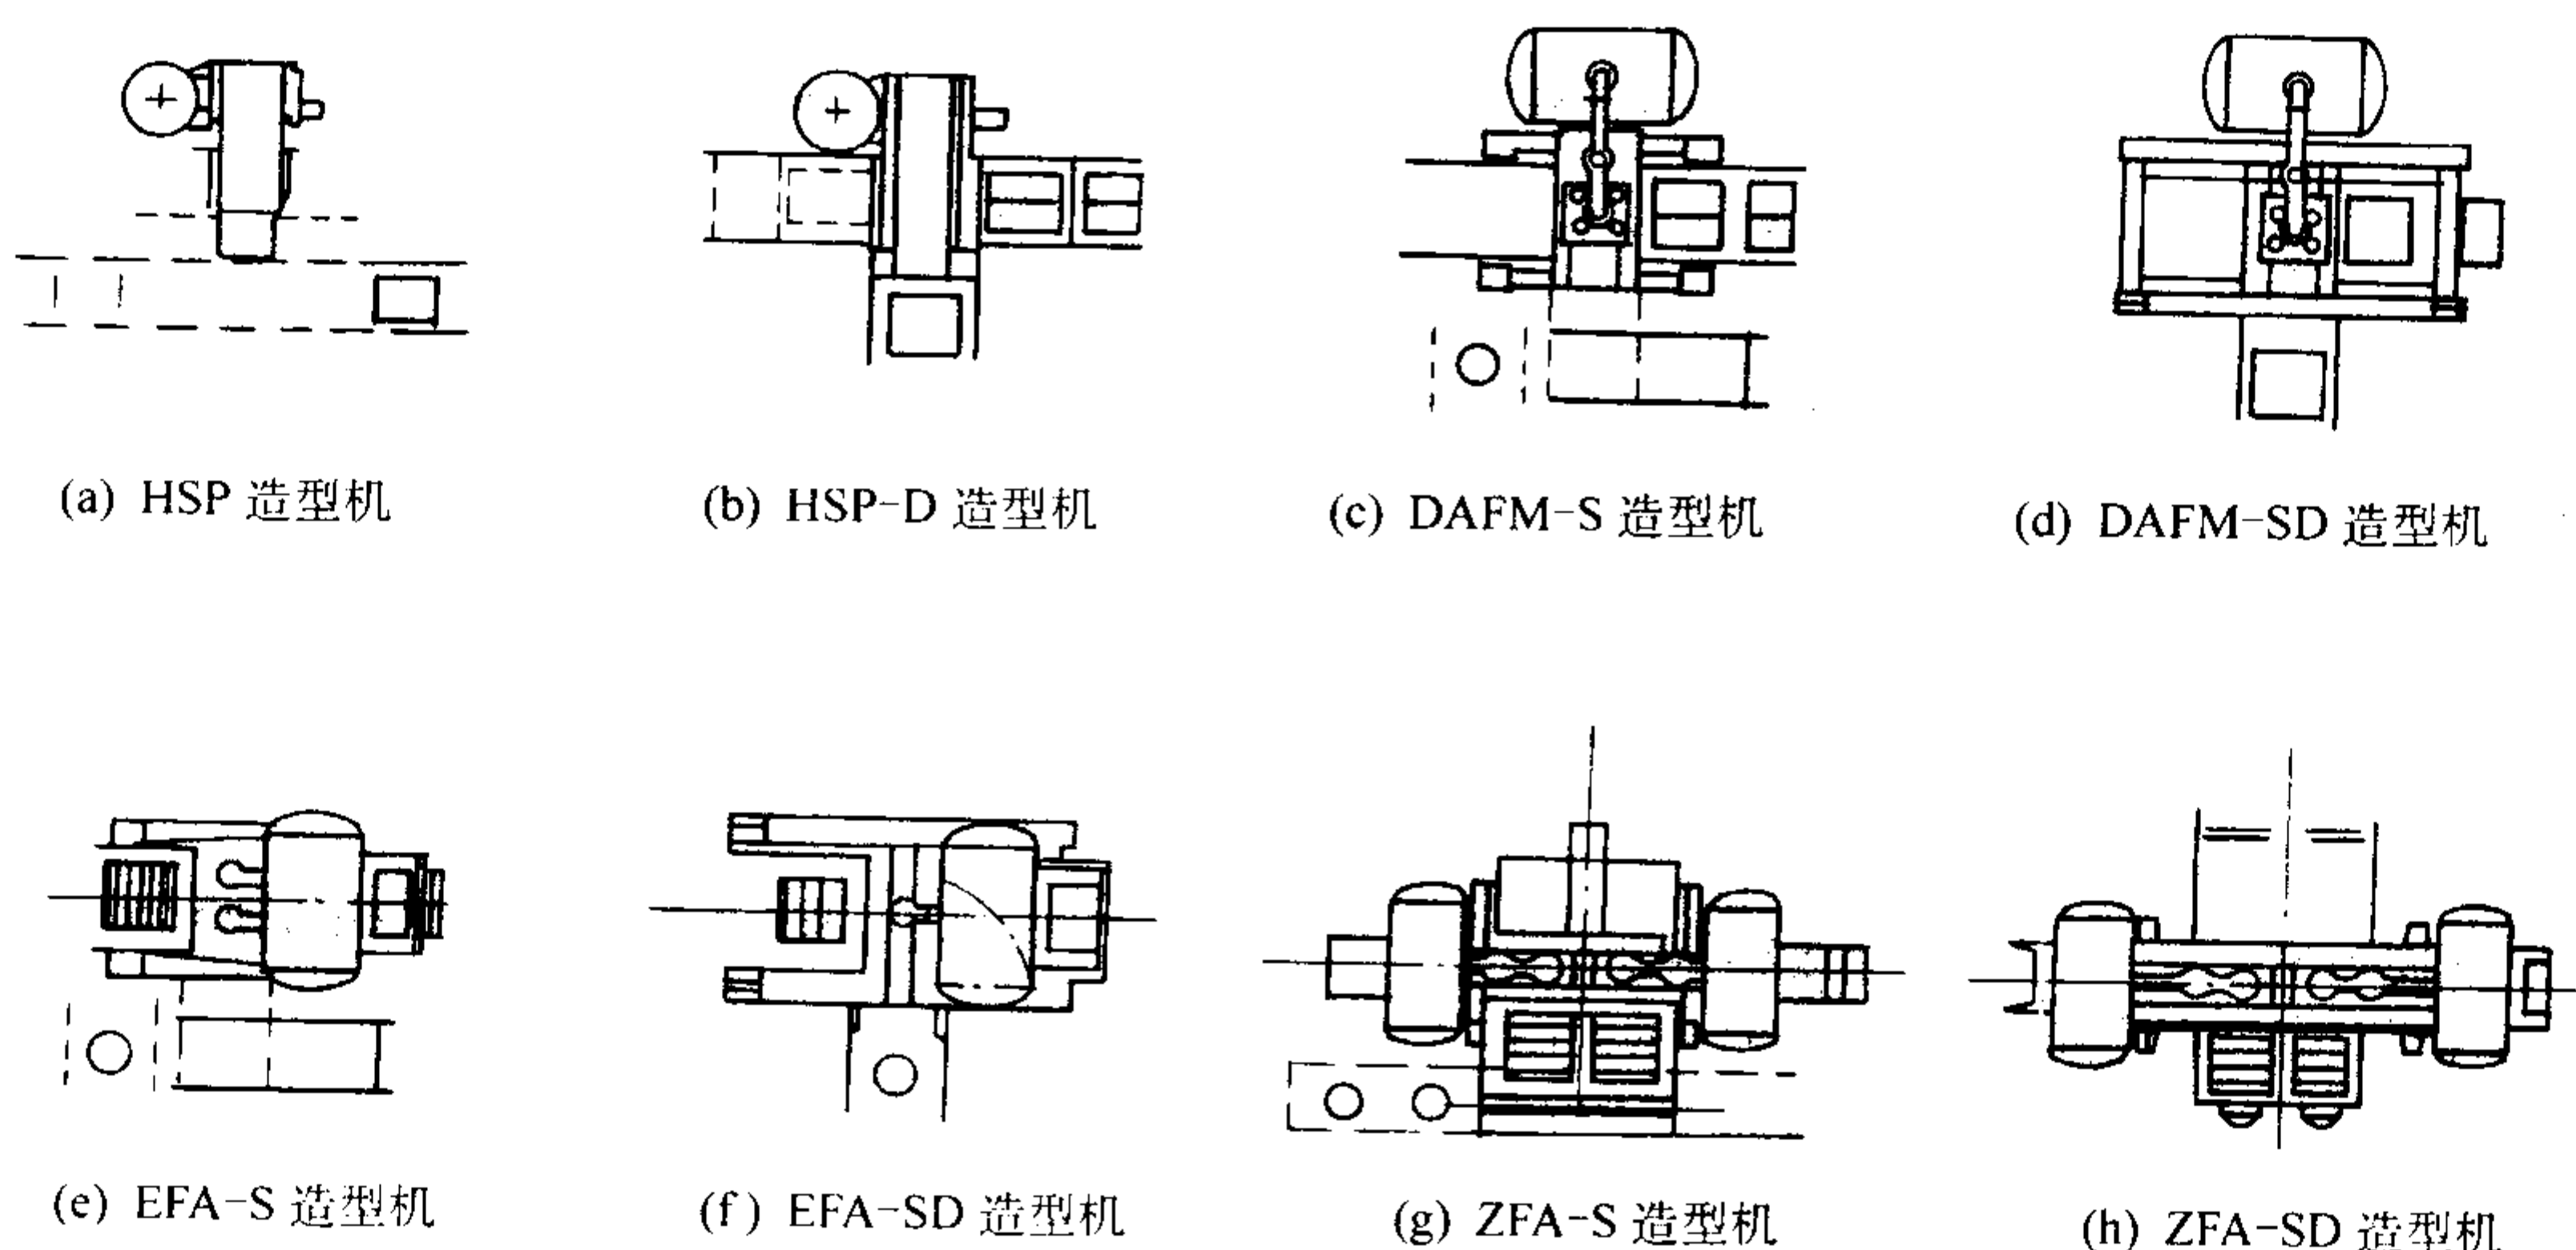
HWS 公司各种型号静压造型机平面布置示意图
